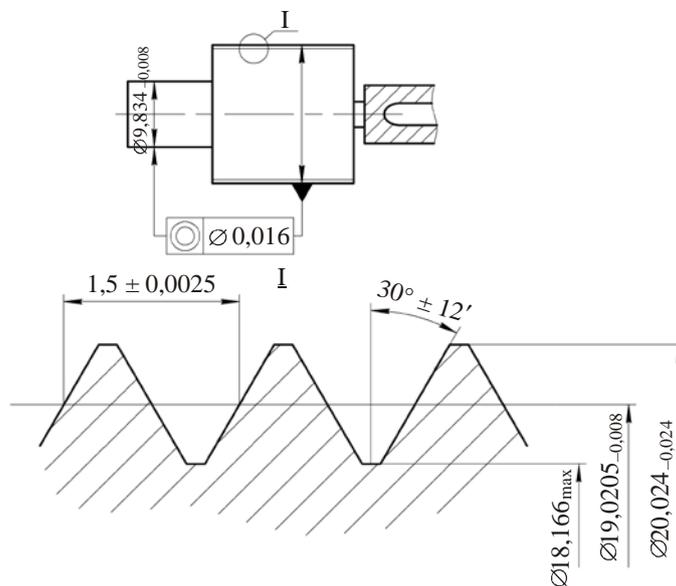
Схема калибра для контроля соосности гладкого и резьбового отверстий
